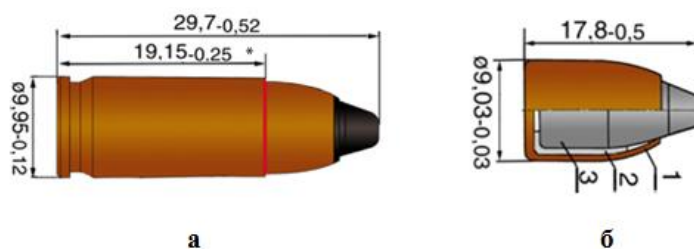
9x19-мм патрон 7Н21: а – патрон; б – пуля; 1 – оболочка; 2 – рубашка полиэтиленовая; 3 – сердечник из стали марки Ст. 70
